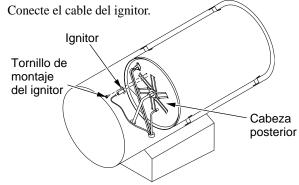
Extracción del tornillo de montaje del ignitor y del ignitor
